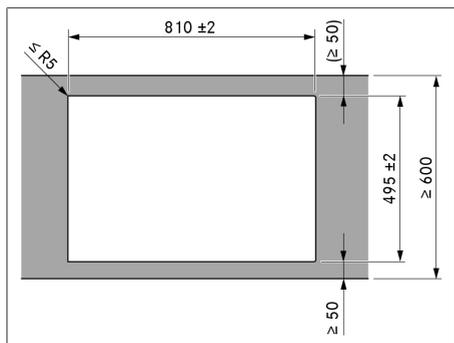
Dimensioni intaglio per montaggio in battuta
